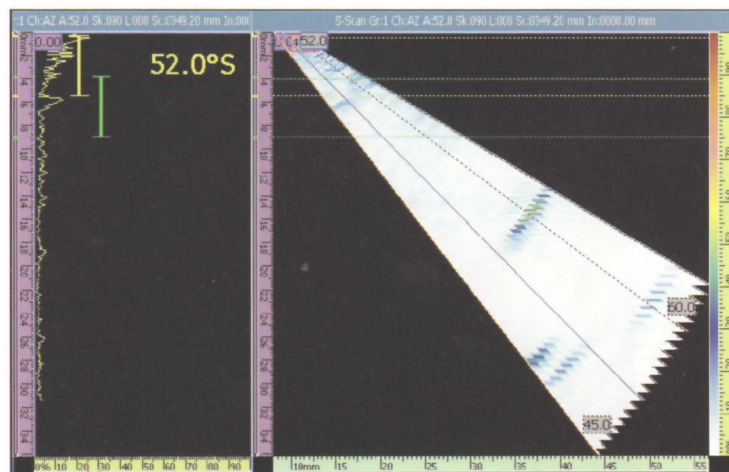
Типичный S-скан сварного шва с образцами непроваров.
